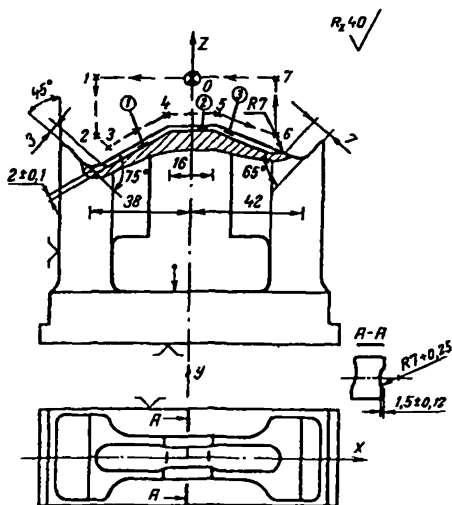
Эскиз детали для примера нормирования операции объемного фрезерования.
